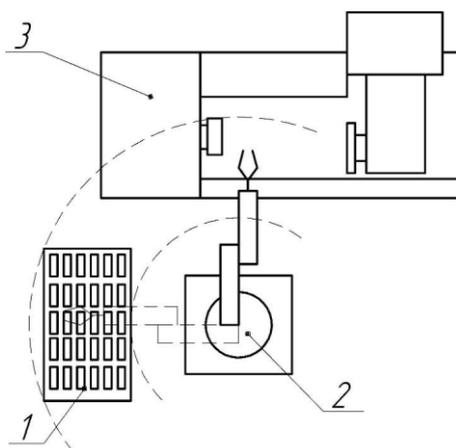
Схема автоматизированной ячейки токарного станка с ЧПУ
